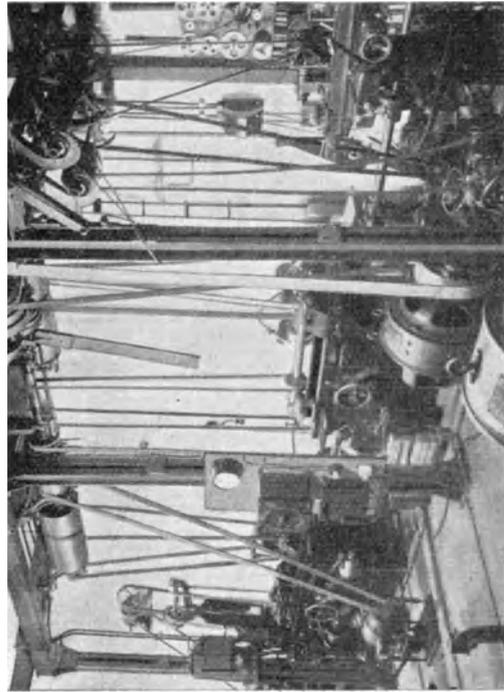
Anbau: Schleifmaschinen, gleichzeitig Versuchstand für Maschinen mit Riemenantrieb.
